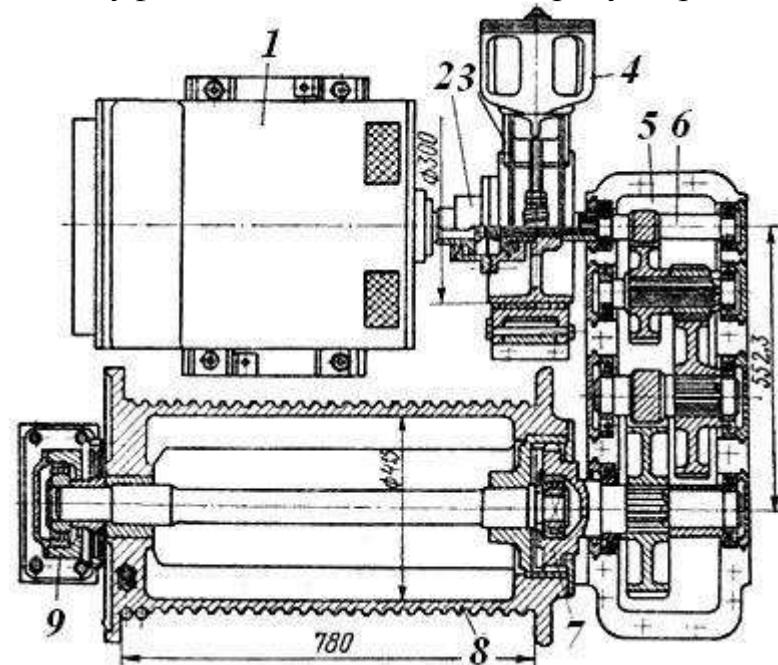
Грузовая лебедка основного подъема: 1 – электродвигатель, 2, 7 – зубчатые муфты, 3 – тормоз, 4 – электромагнит, 5 – редуктор, 6 – входной вал, 8 – барабан, 9 – опора барабана
